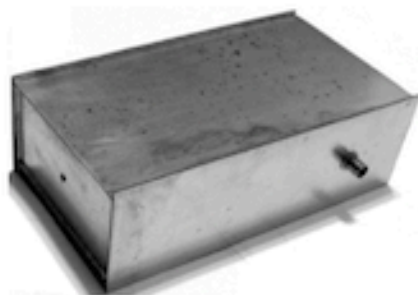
Фото корпуса СУ в сборе. На боковых стенках установлены розетки РЧ соединителей типа BNC. На передней торцевой стенке в её центре видно отверстие под ось КПЕ, пока, к сожалению, отсутствующего (с большим зазором)
